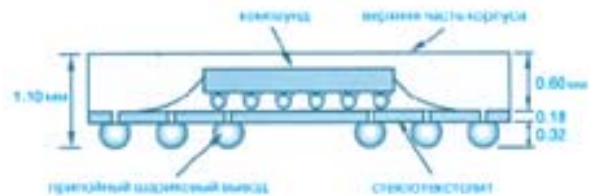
Микросхема в корпусе CSP с кристаллом flip-chip
